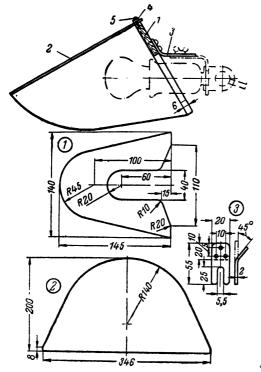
Чертежи подставки под осветитель. a — общий вид; δ — детали (1 — основание; 2 — кронштейн; 3 — бровки).
